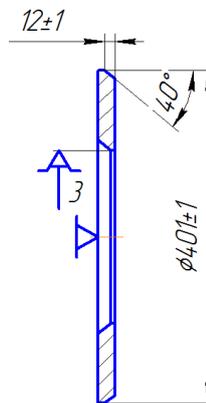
Эскиз базирования заготовки на 010 токарной операции.
